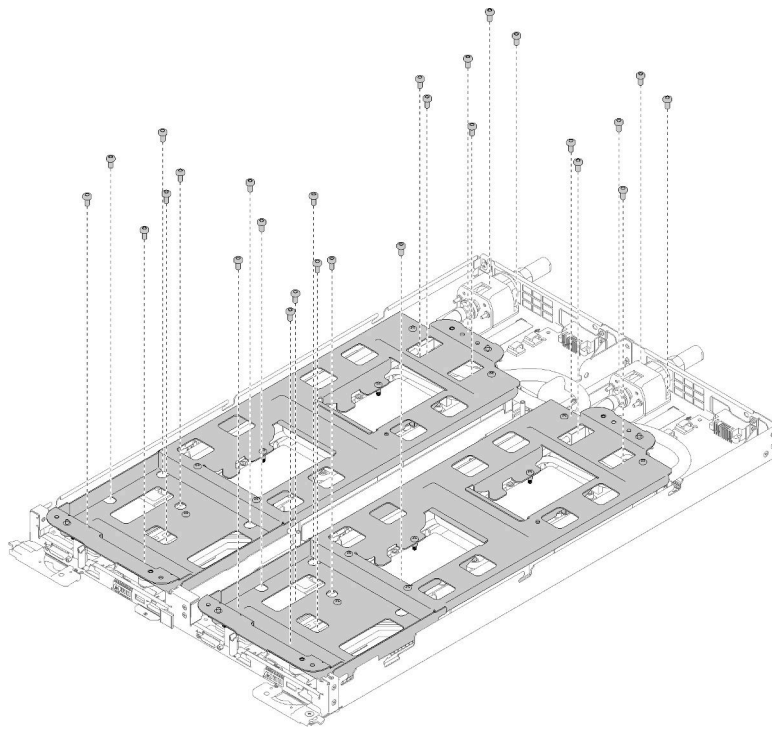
Positionen der silbernen T10-Torx-Schrauben zum Befestigen des Wasserkreislaufs
